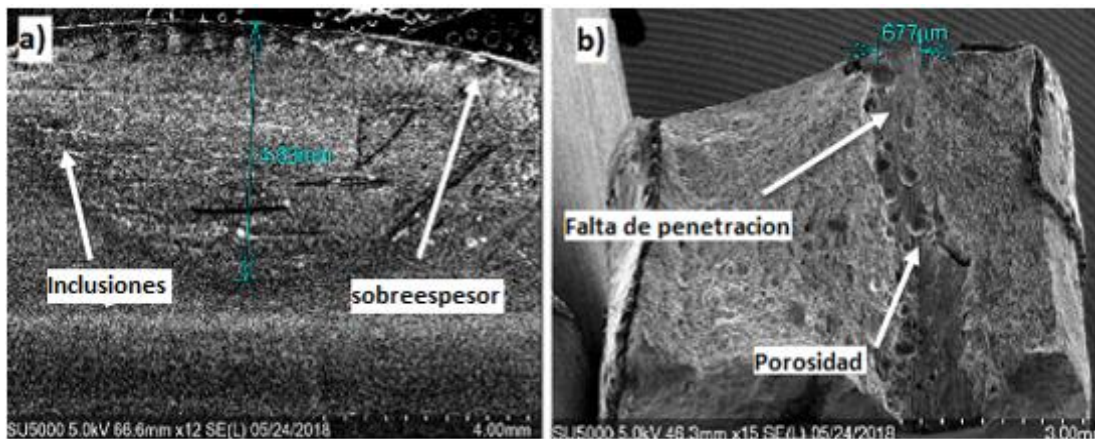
Imágenes por SEM (a) Imagen frontal junta soldada a (389 J/mm) (b) fractura superficial en probeta de tensión soldada a (356 J / mm).
